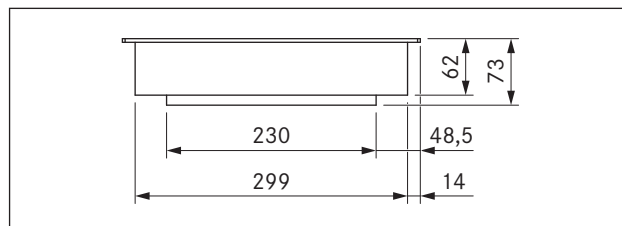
CKT dimensioni apparecchio vista frontale
